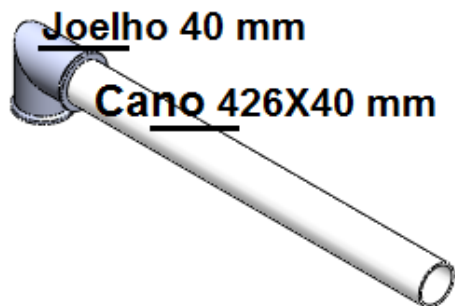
Montagem dos módulos – Módulo 4 – Passo 5
